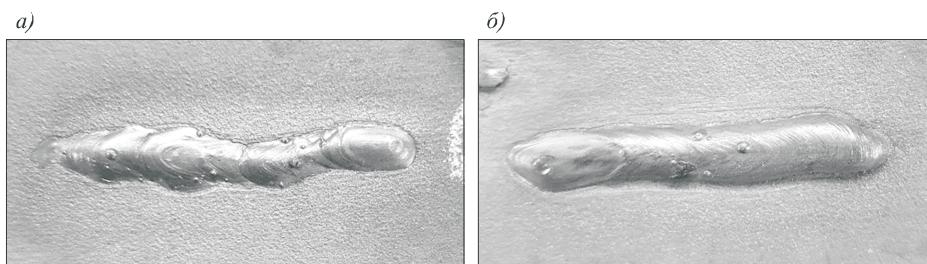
Внешний вид наплавленного валика на оцинкованную поверхность стального профиля при различной технике сварки
